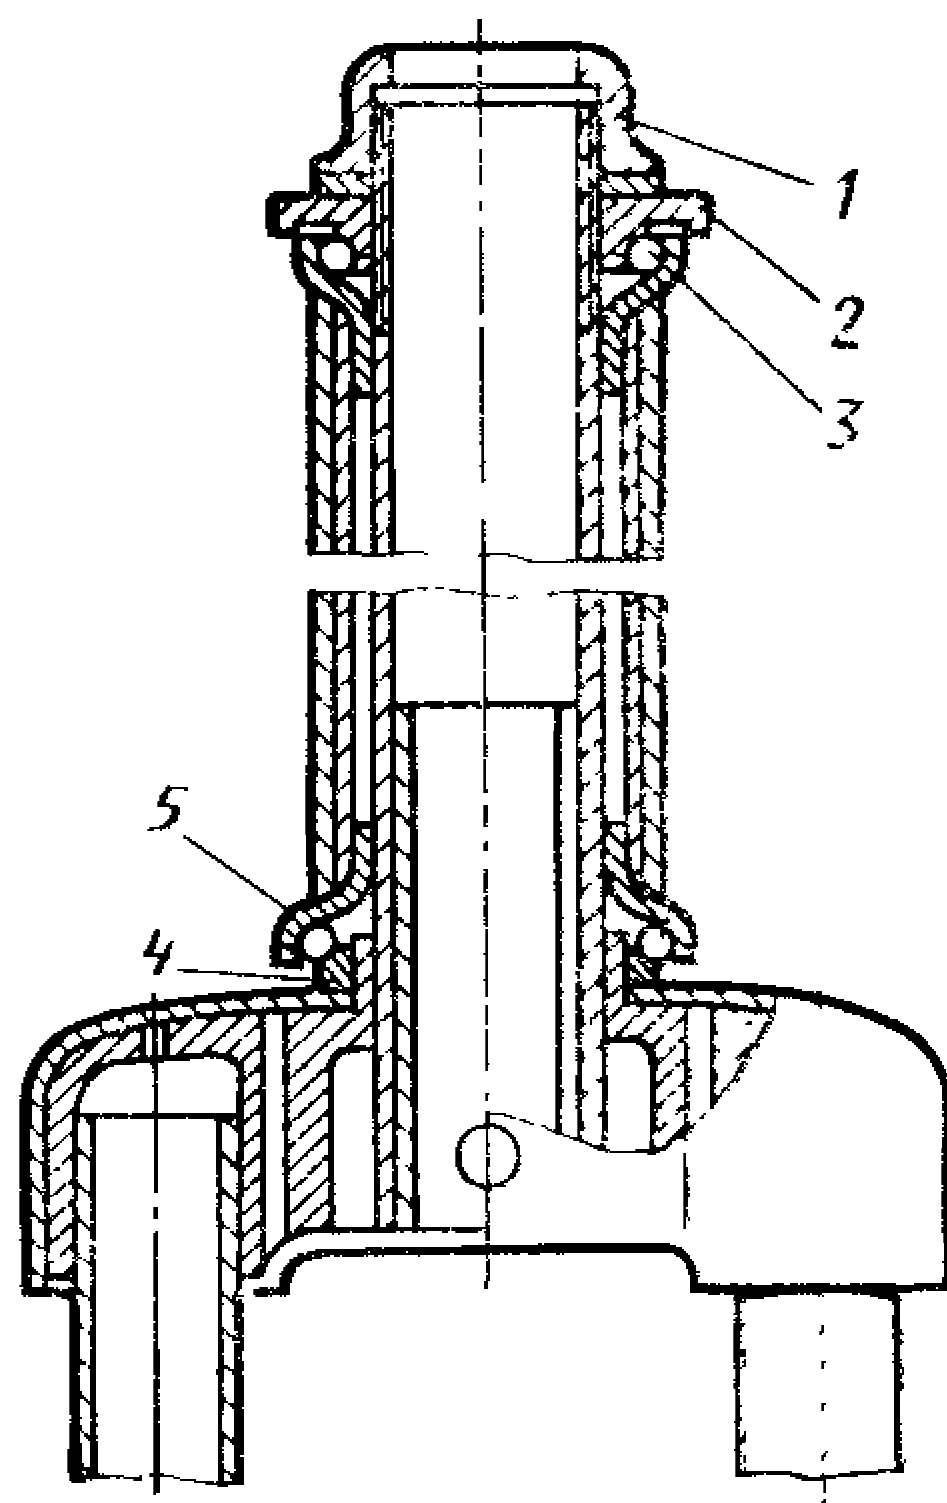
Передняя вилка в сборе с шарикоподшипниками:
